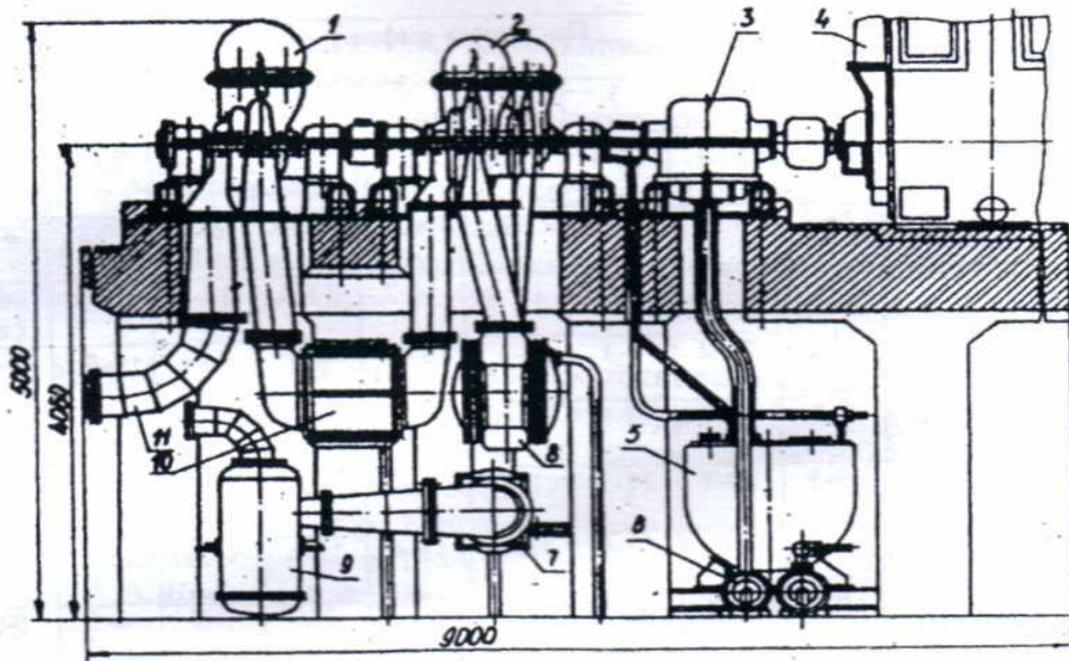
Общий вид компрессорной установки ЦК-135/8М
